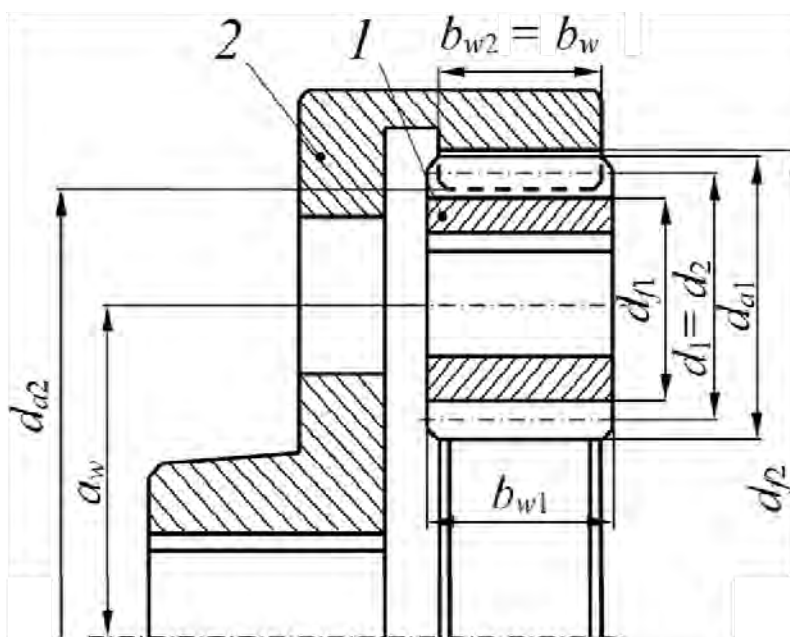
Геометрические параметры цилиндрической зубчатой передачи с внутренним зацеплением: 1 – шестерня; 2 – колесо
